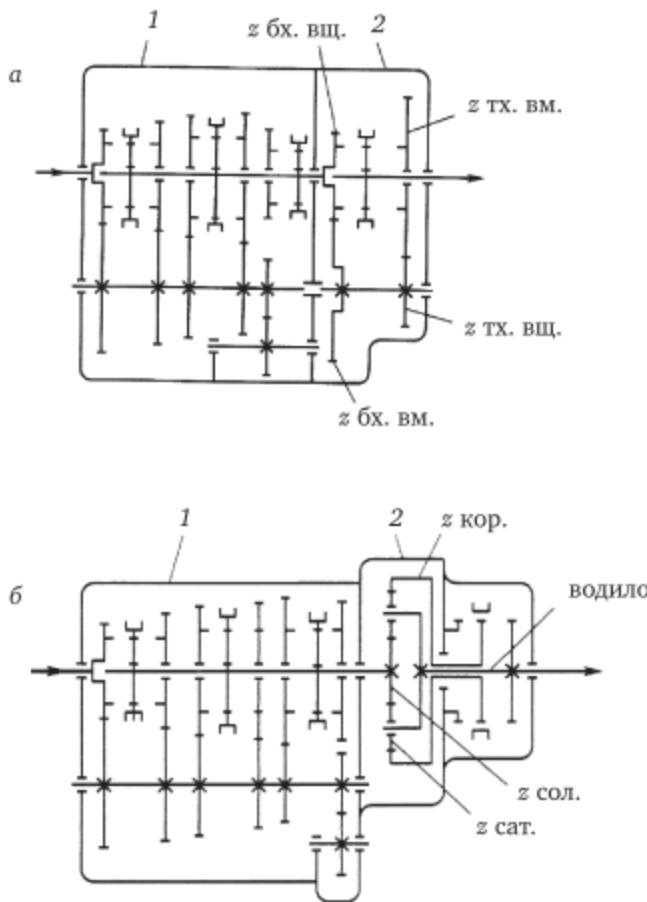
Схемы многоступенчатых коробок передач с дополнительным редуктором:
